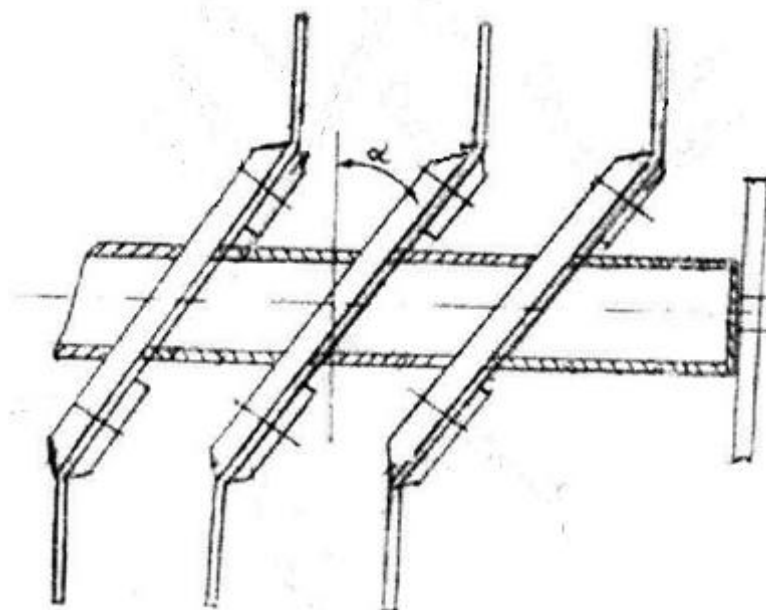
Вал измельчающего барабана с закрепленными дисками:
